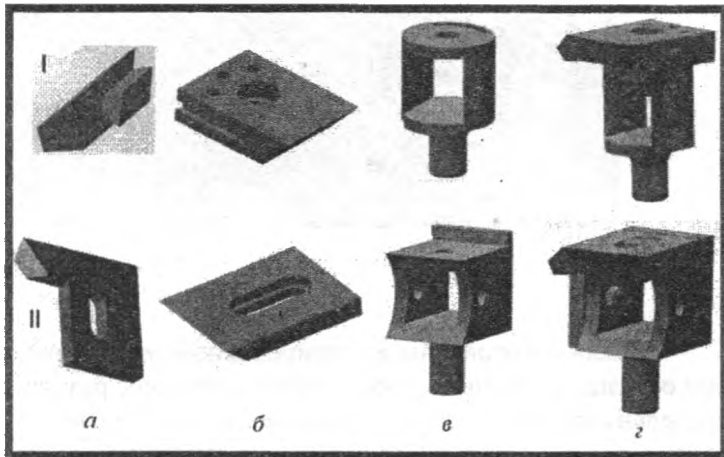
Новые конструкции двухлезвийных резцов: а – подрезающий короткий резец; б – подчищающий длинный резец; в – резцедержатель; г – составной двухлезвийный резец в сборе
